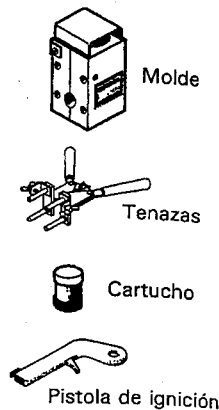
Equipo de soldadura aluminotérmica. (Cortesía KLK).
